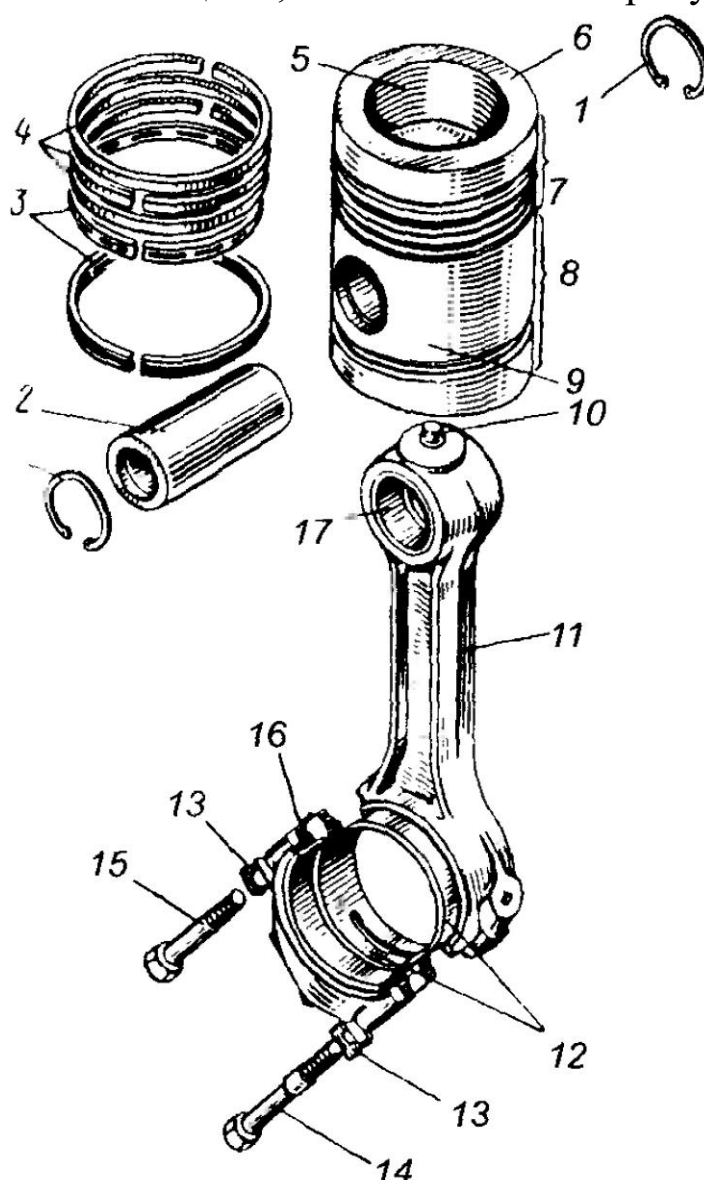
Детали шатунной и поршневой группы двигателя ЯМЗ-238
